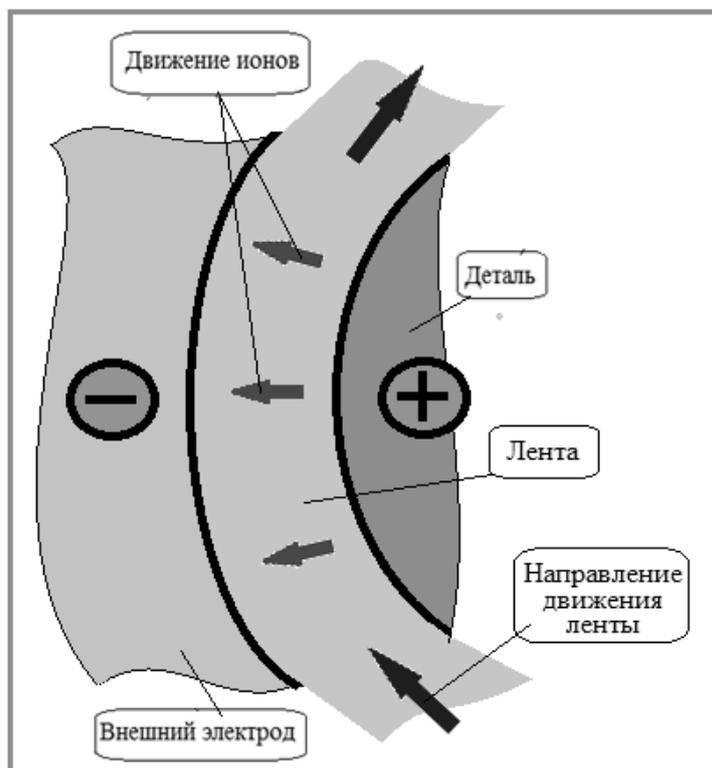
Схема обработки поверхности детали лентой (СЭПЛ)
